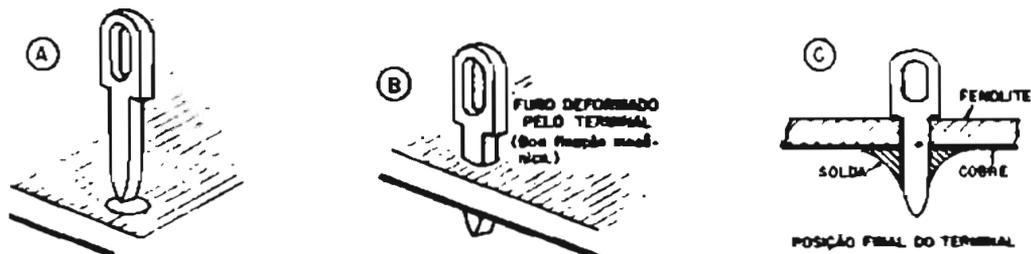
Modo correto de inserir e soldar os terminais na placa de fiação impressa
